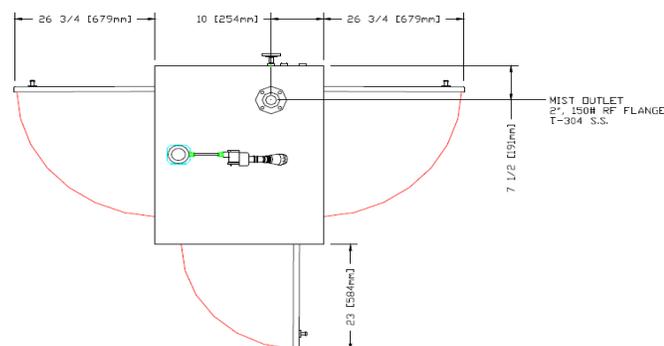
Vista de planta de la consola de generación. [10]
